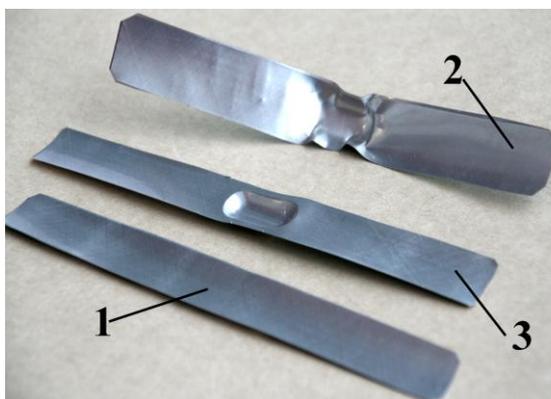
Варианты обработки заготовки вытяжкой.
